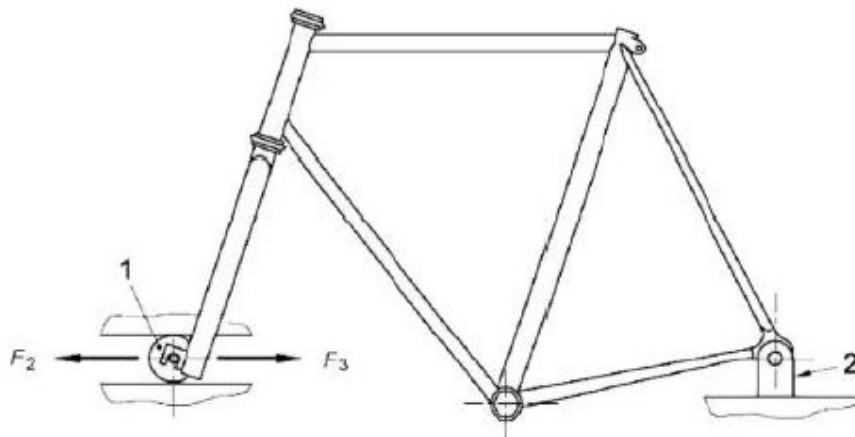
Posición de ensayo del conjunto cuadro-horquilla. Ensayo por fuerzas horizontales.
